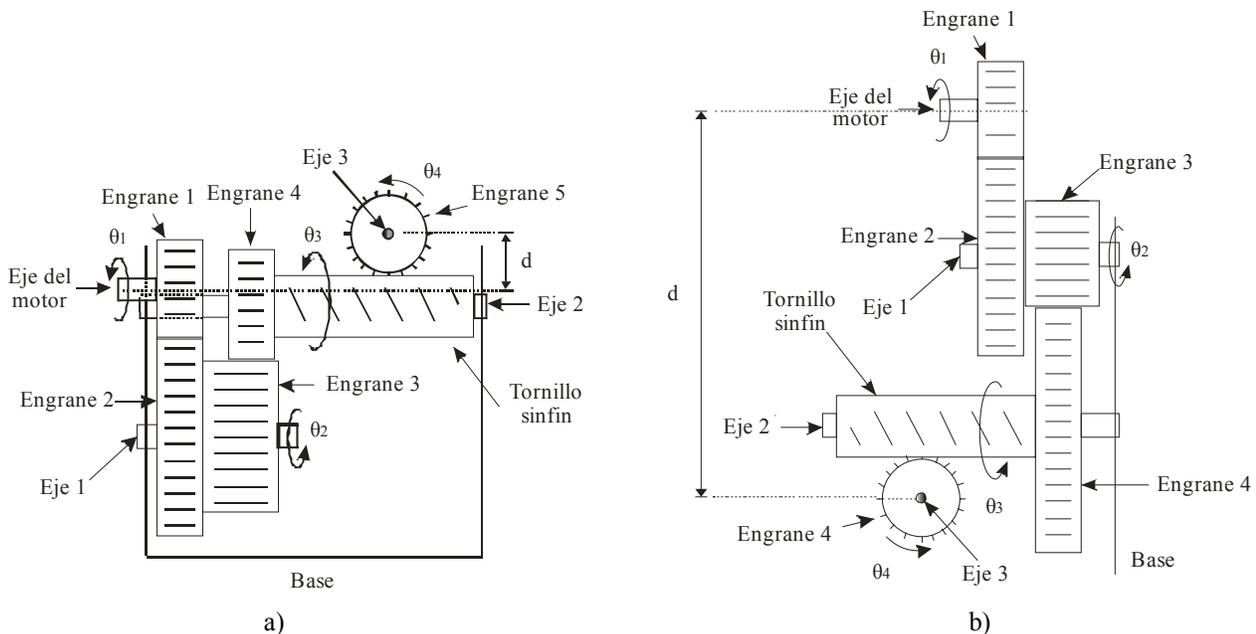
Sistema de engranes: a) Engranaje Pan, b) Engranaje Tilt.
